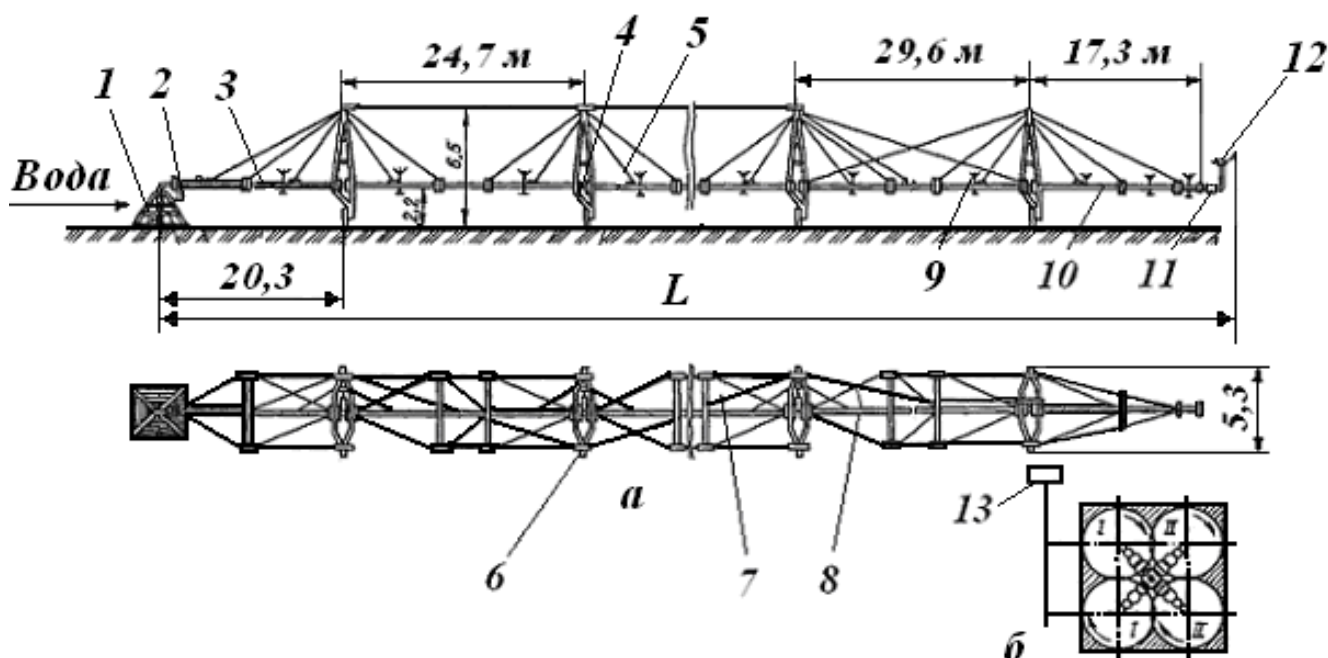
Дощувальна машина «Фрегат»: а - загальний вид; б - схема поливу двох машин на двох позиціях; 1 - нерухома опора; 2 - стоп-пристрій; 3 - водопровідний трубопровід; 4 - візок; 5, 6, 7 і 8 - відповідно системи тросів, автоматичного регулювання швидкості руху візка, механічного та електричного захисту; 9 - дощувальні апарати; 10 - зливний клапан; 11 - система відключення кінцевого апарата; 12 - кінцевий дощувальний апарат; 13 - насосна станція
